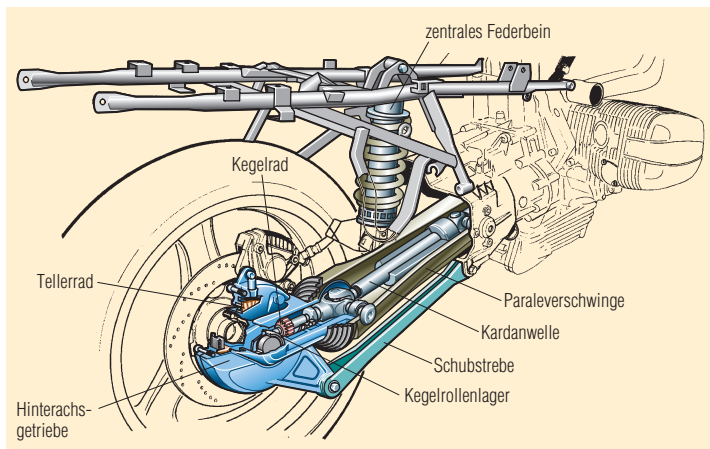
Einarmschwinge mit Schubstrebe (Paraleverschwinge).
